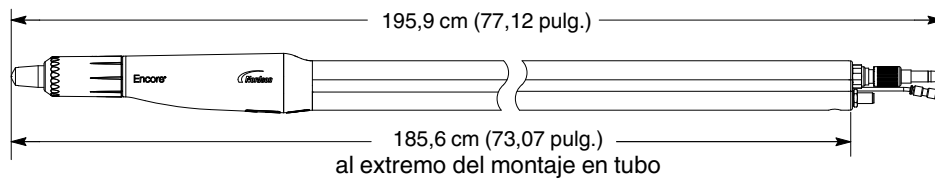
Dimensiones y pesos de las pistolas automáticas Encore
